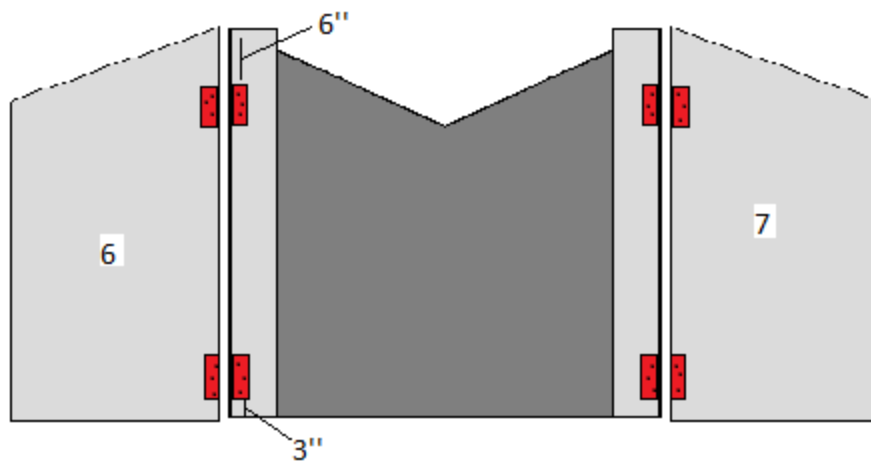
Étape 7 : Assemblage des portes par les charnières du prototype 3
